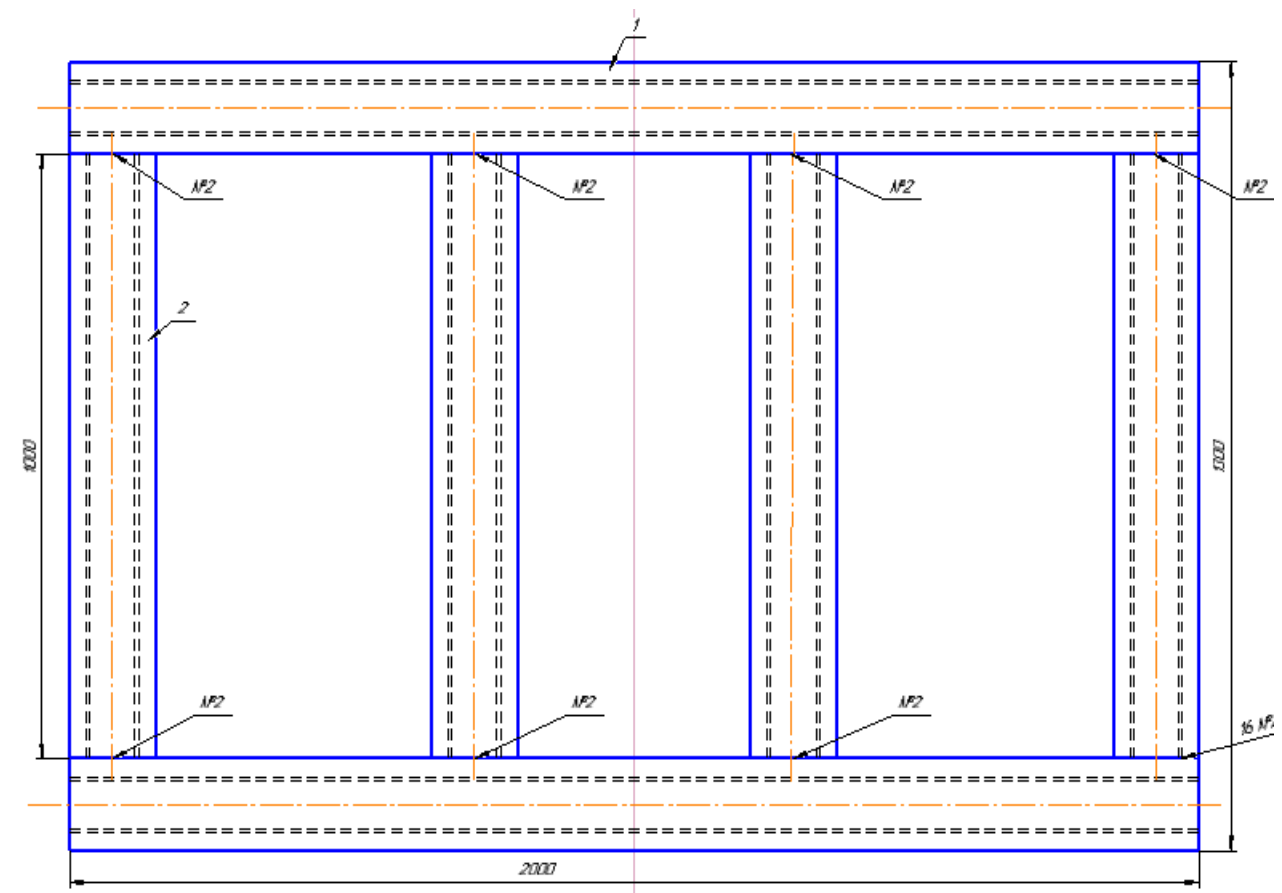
Стелаж із балок коробчастого перерізу
